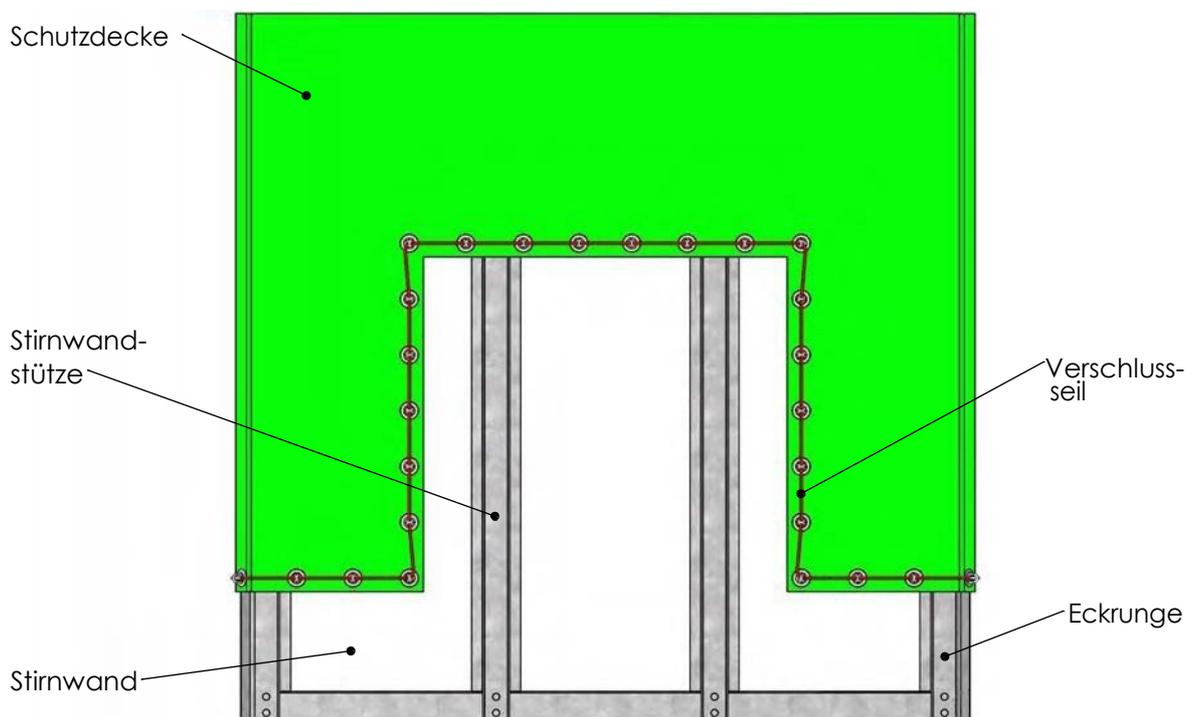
Stirnwand: Schutzdecke mit Ausschnitt
